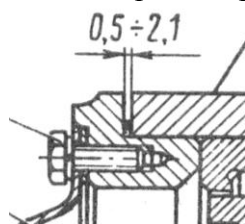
Эксплуатационный зазор между торцевой поверхностью буксы и фланцевой поверхностью крышки крепительной в зоне расположения ушков.
